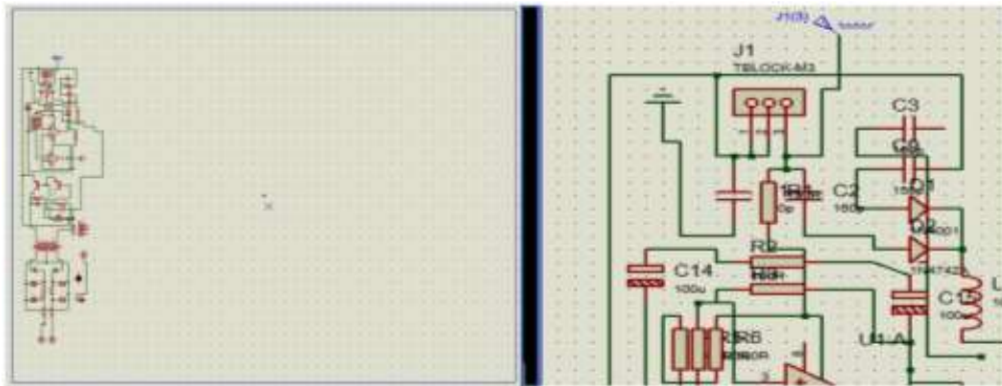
Dimensionado de la tarjeta, colocación y conexión de componentes.
